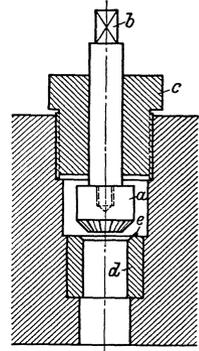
Fräs Werkzeug für die Ventilsitze.
